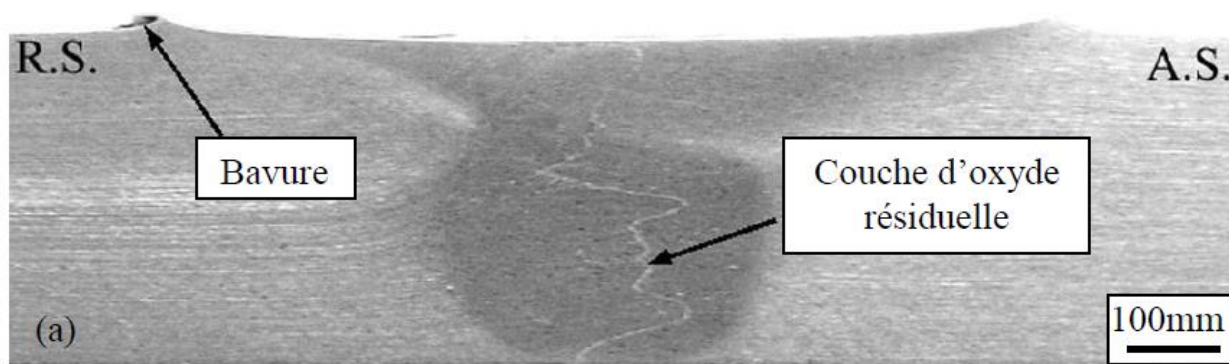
Coupe transversale dans un joint FSW qui montre les bavures et les lignes d'oxydes [II-30]
